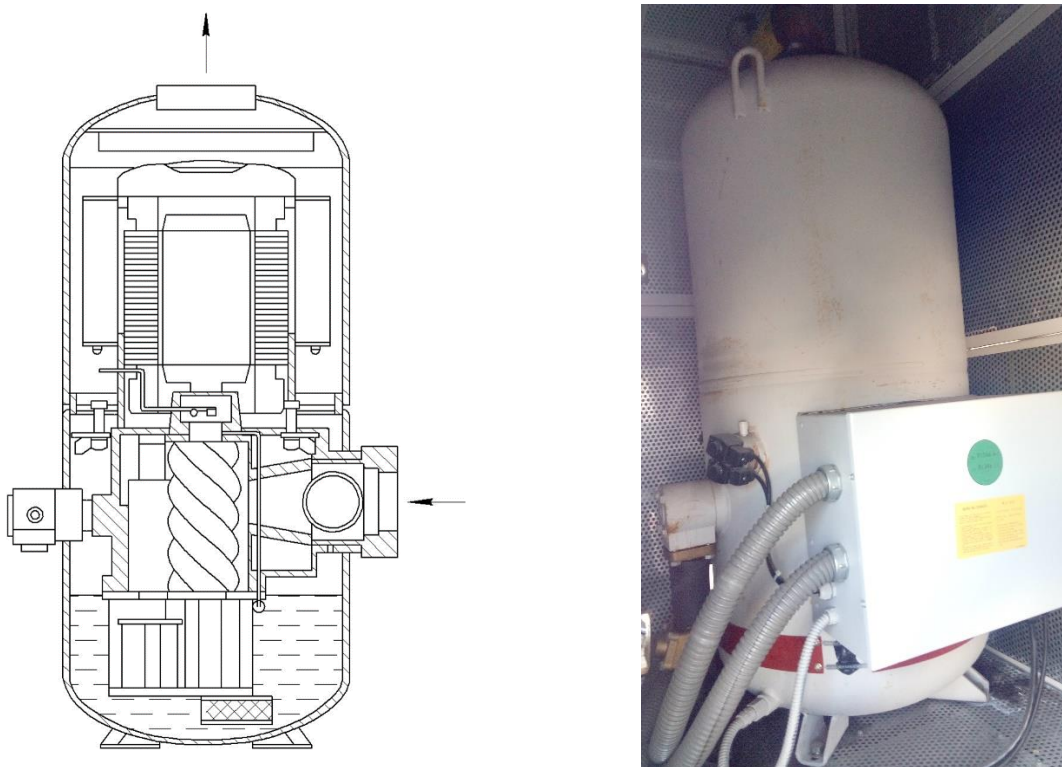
Герметичный вертикальный винтовой компрессор
